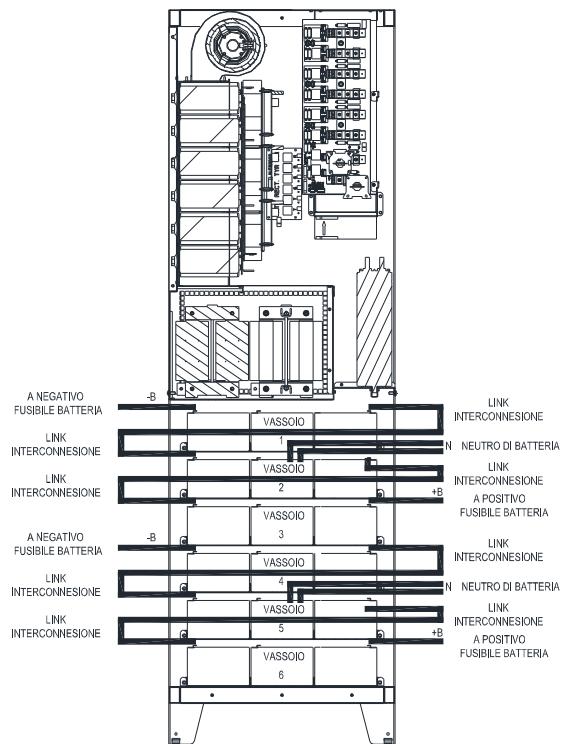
12/14Ah 12V connessione vassoi batterie vista frontale
